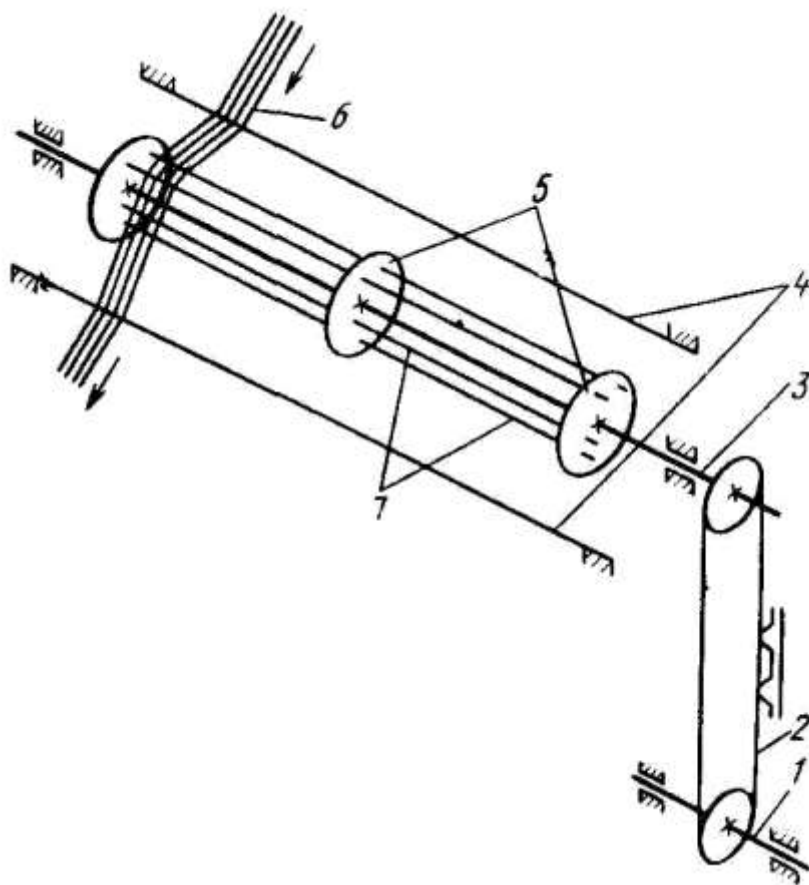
Схема ротаційного нитконатяжного пристрою активної дії
